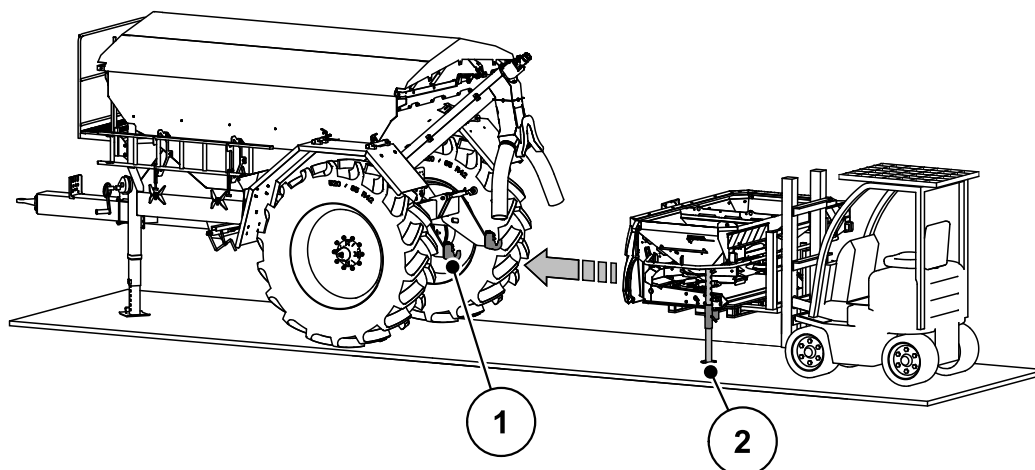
Trzypunktowy system drążków TWS 7010
